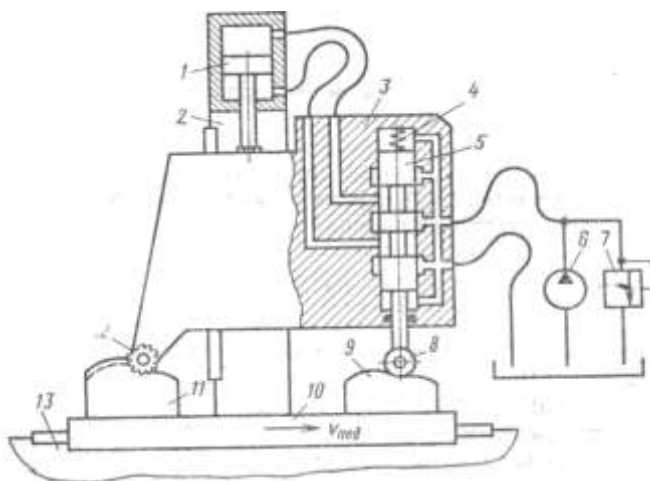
Схема следящего гидропривода копировально-фрезерного станка
